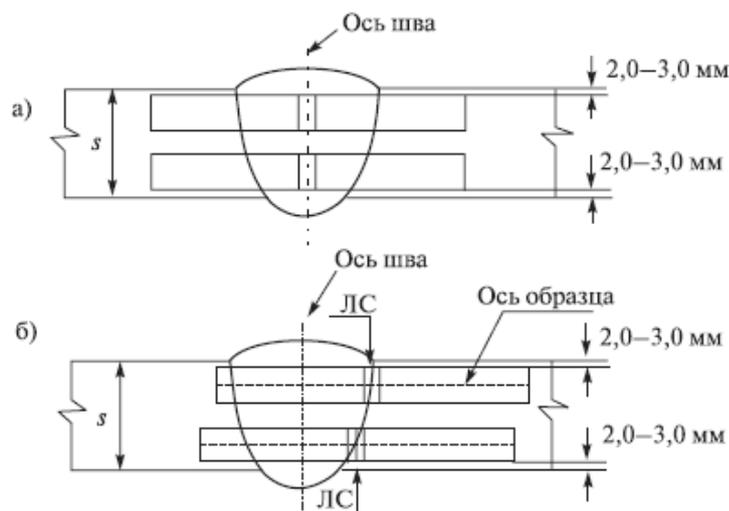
Форма и размеры образцов на ударный изгиб
